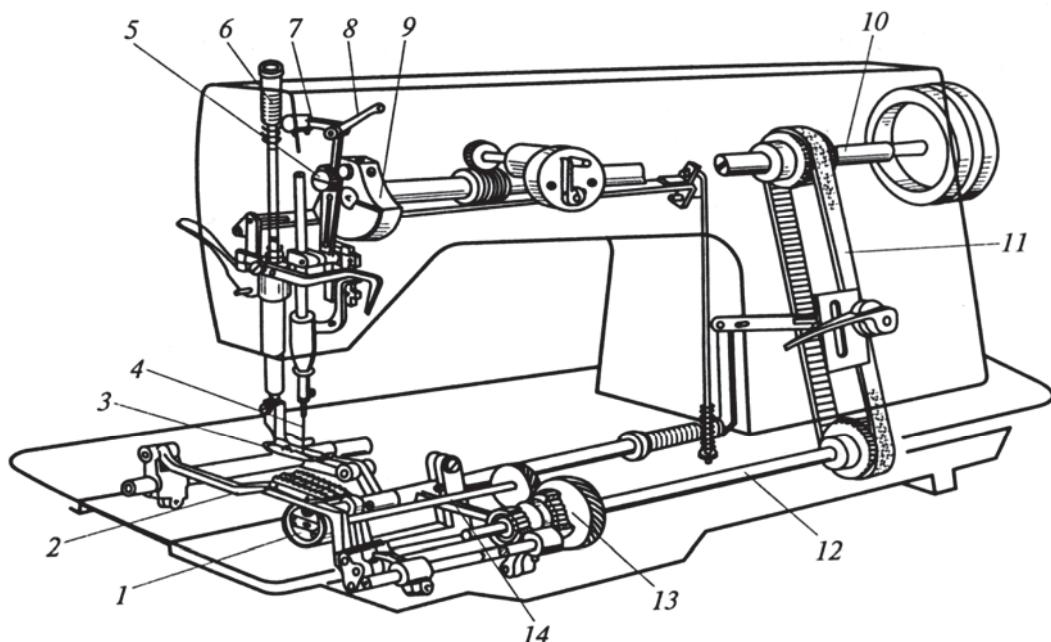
Конструктивно-кінематична схема механізмів швейної машини КУР-1022 М:
